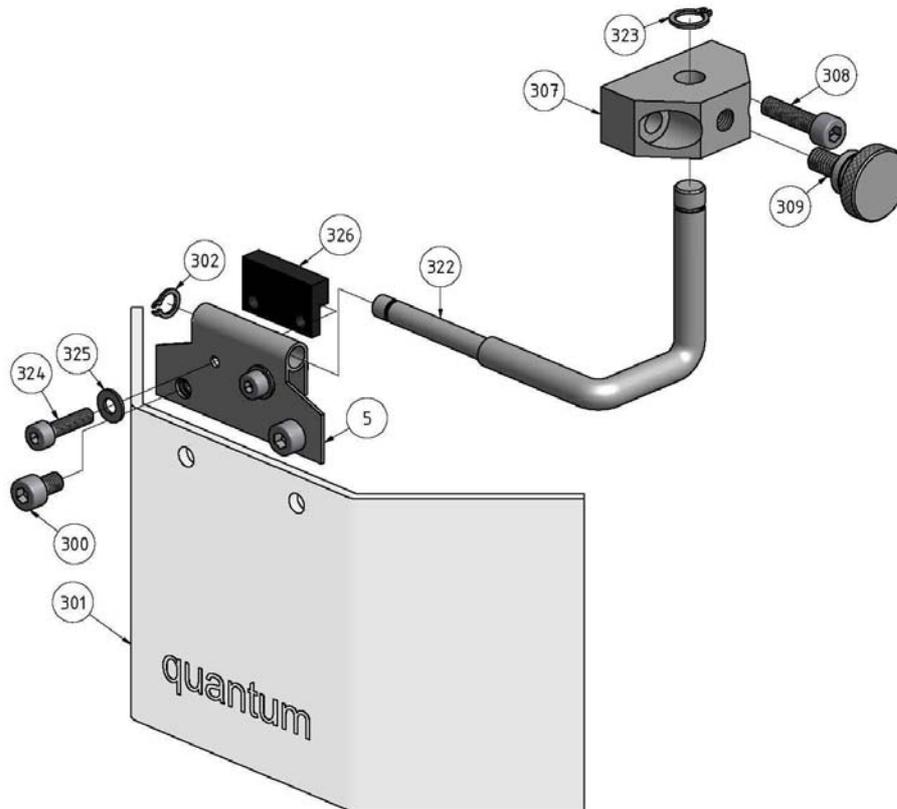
Fräsfutterschutz - Milling chuck protection
